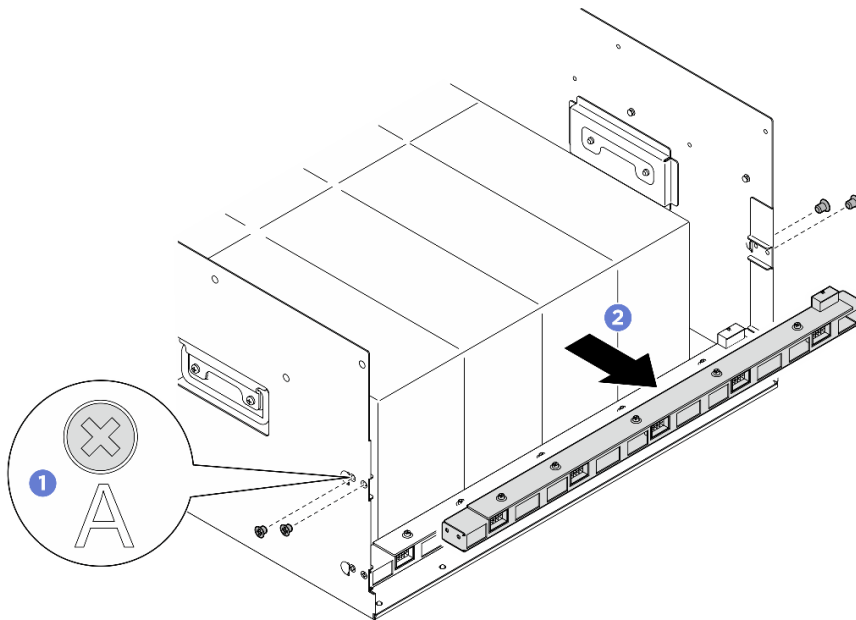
Remoção do conjunto de placa de controle do ventilador traseiro
